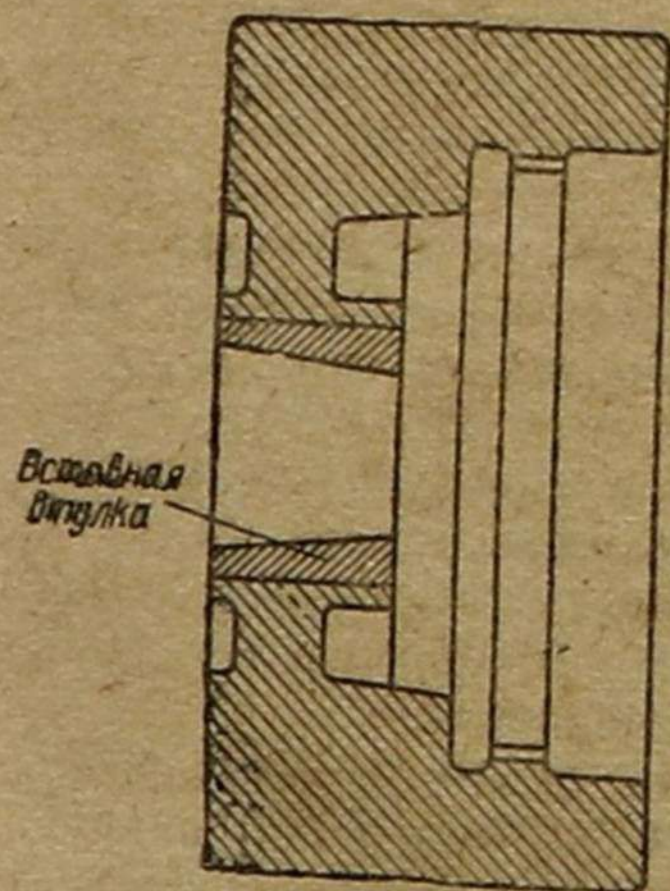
Установка втулки в ступицу маховика пускового двигателя
